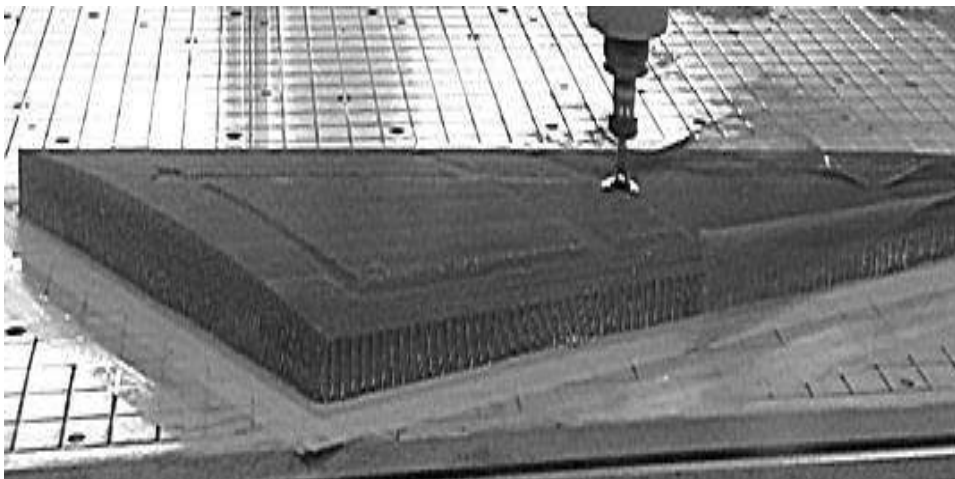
Чорнове фрезерування торців стільникового блока
